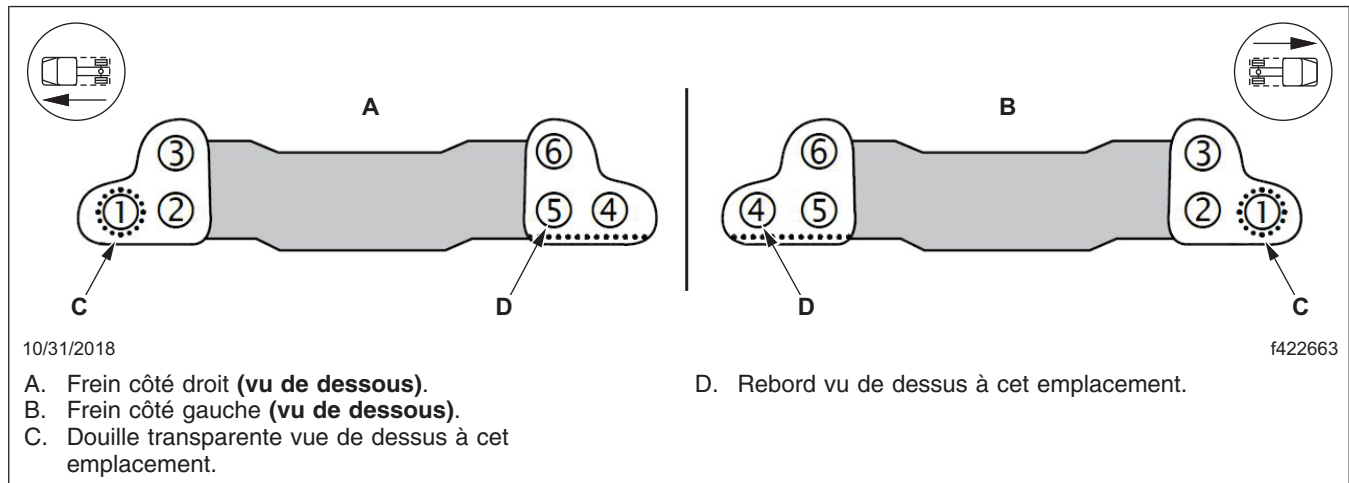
, Séquence de serrage (vue de dessous), étrier Bendix à montage radial
